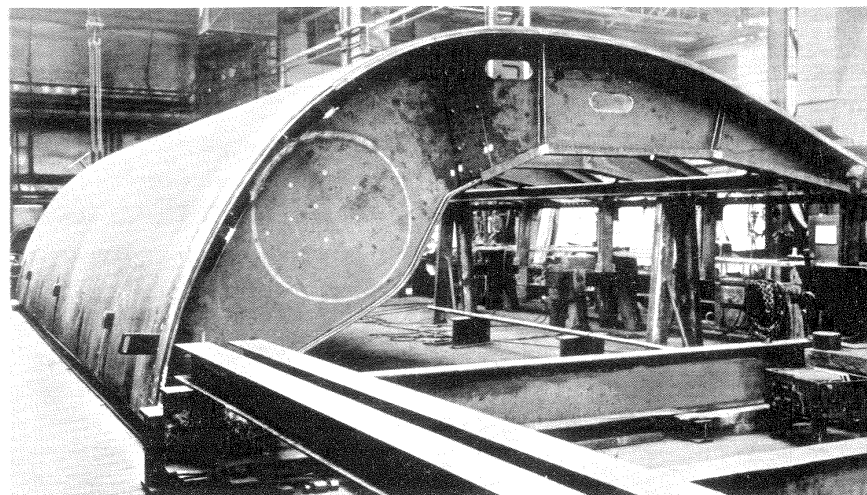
Hoja inferior de una compuerta de tejado ya soldada en los talleres Voith, Alemania. Pueden verse a la izquierda los trinquetes del dispositivo de enclave y delante un trinquete de emergencia.
